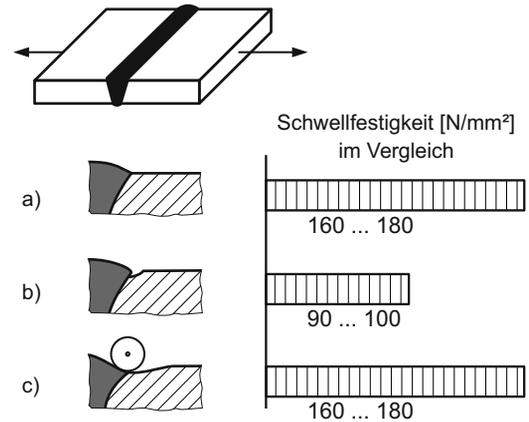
Die Wirkung von Kerben auf die Schwellfestigkeit von Bauteilen bzw. Schweißverbindungen zeigen die Bilder 2.9 bis 2.12.
